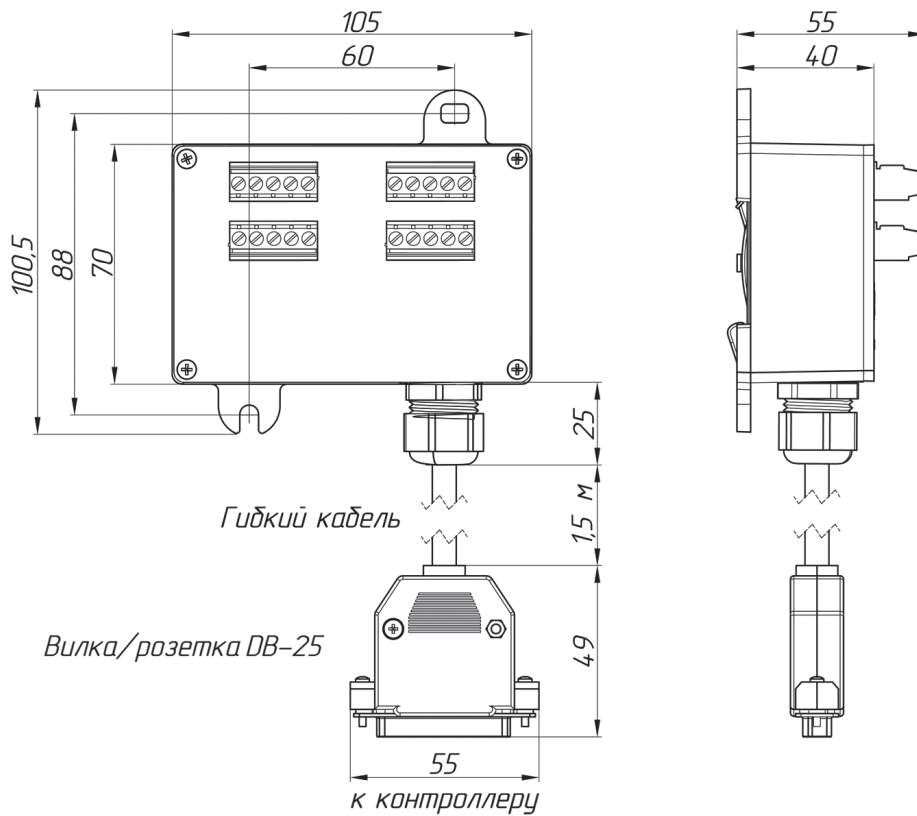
Внешний вид коробки клеммной: код вида 11, 14
